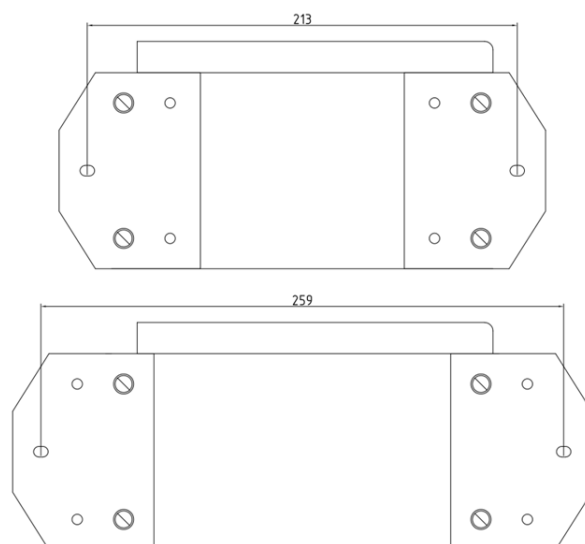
Установочные размеры реле РТС-80 в стандартном корпусе с комплектом адаптации.
